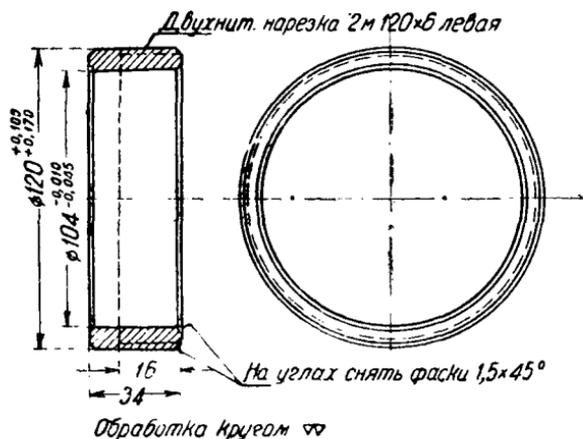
Дет. 167. Кольцо отражателя с левой резьбой
